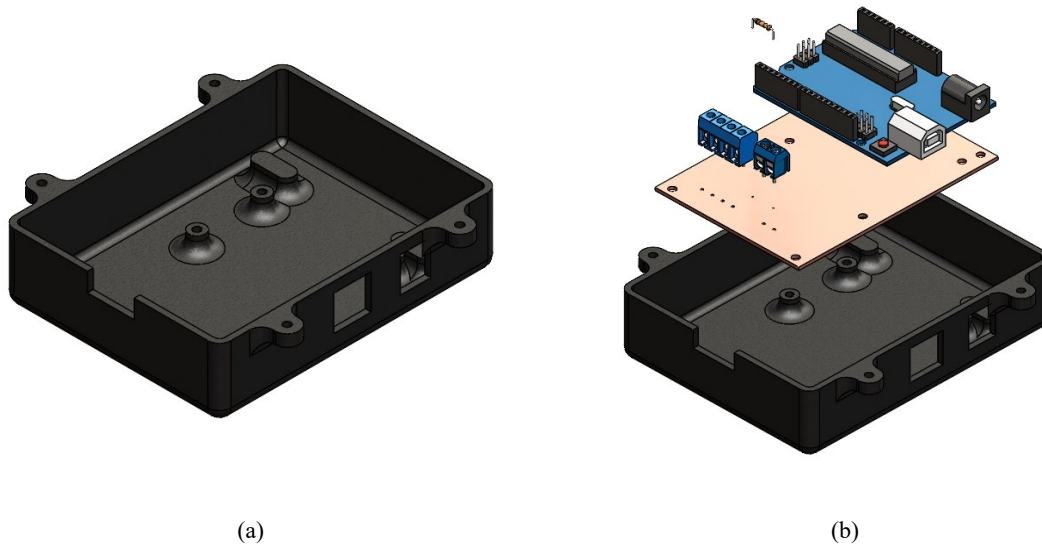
Diseño del componente en SolidWorks 2025: (a) diseño de la carcasa y (b) vista explosionada de la carcasa con sus componentes electrónicos.
